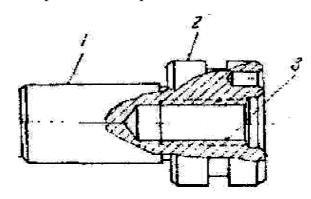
Ось промежуточной шестерни замедленной передачи
